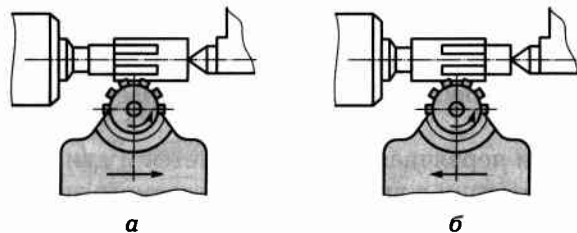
Схемы попутного (а) и встречного (б) фрезерования зубьев
